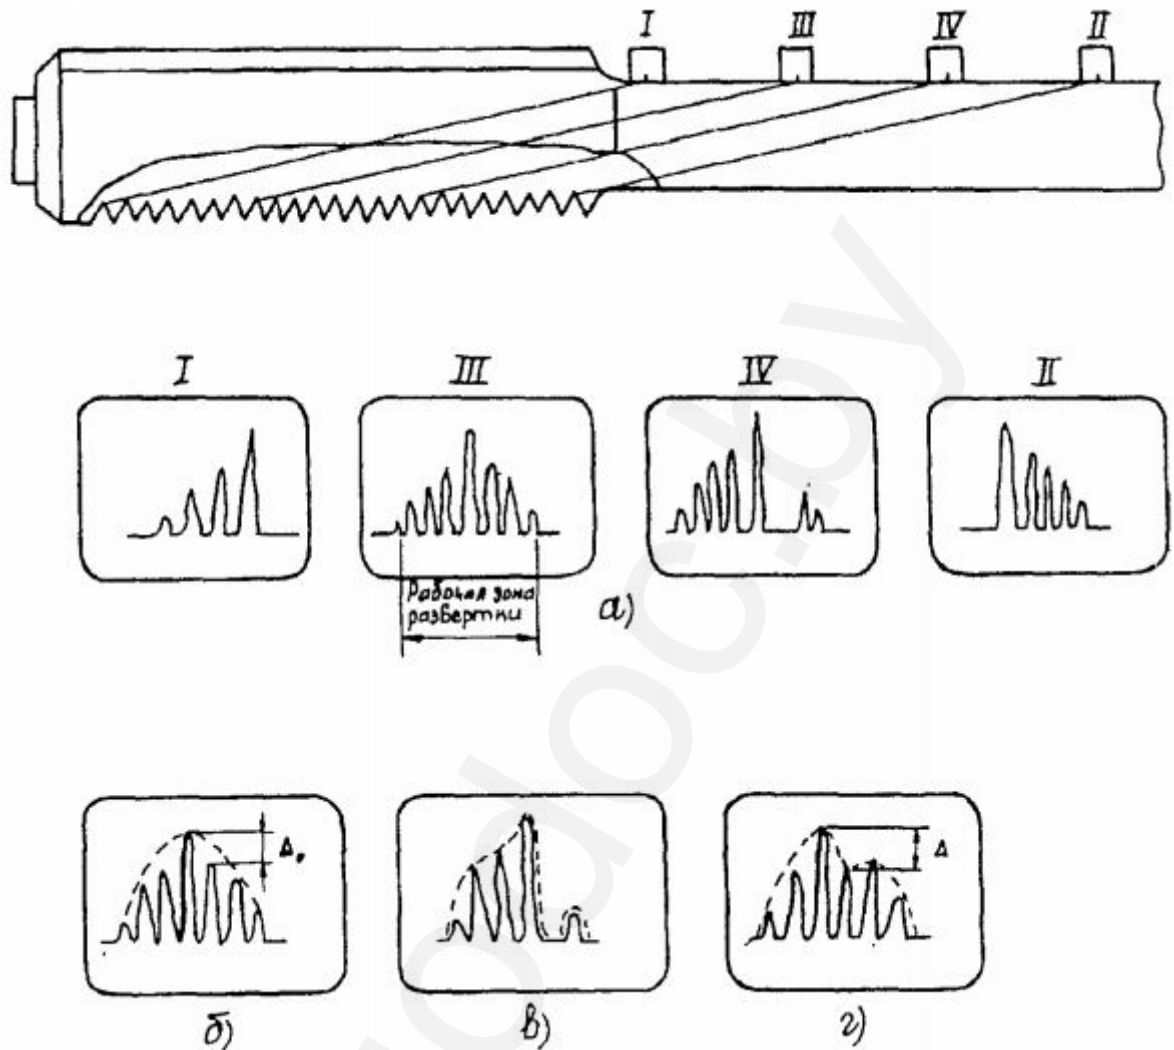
Схема контроля шпильки без осевого сверления:
